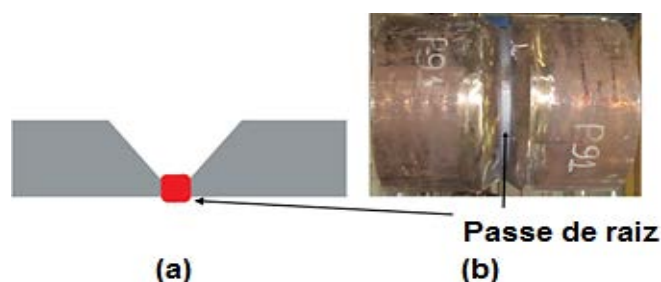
Passe de solda de raiz em uma junta – terminologia usual de soldagem e símbolos de solda – (MARQUES, MODENESI, BRACARENSE) – UFMG – Julho- 2007.
